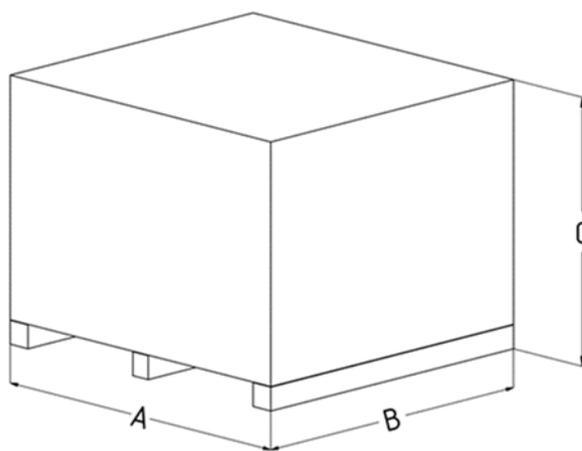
Габаритные размеры воздухонагревателя в упаковке
